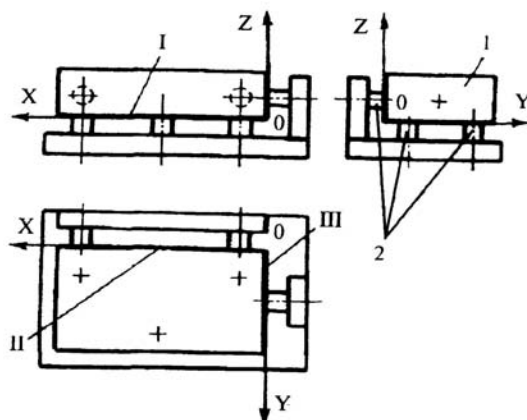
Пример реализации закрепления плоской заготовки
